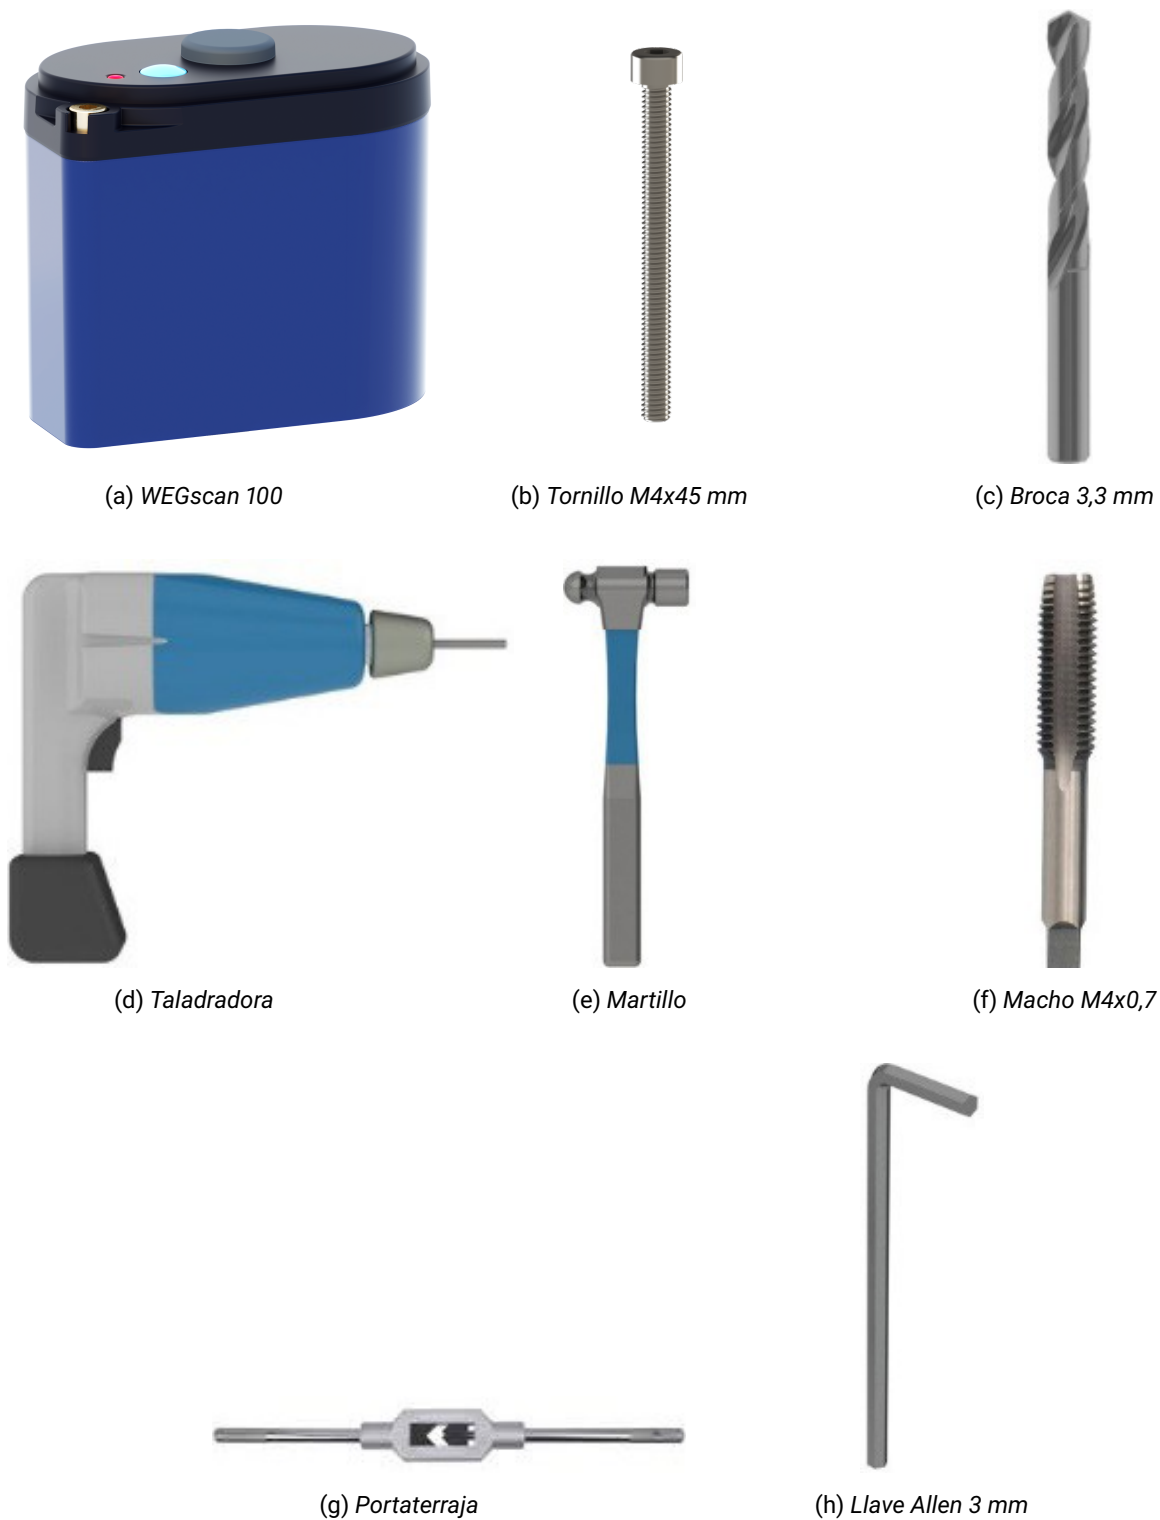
Herramientas y materiales necesarios para la instalación del sensor en el motor
